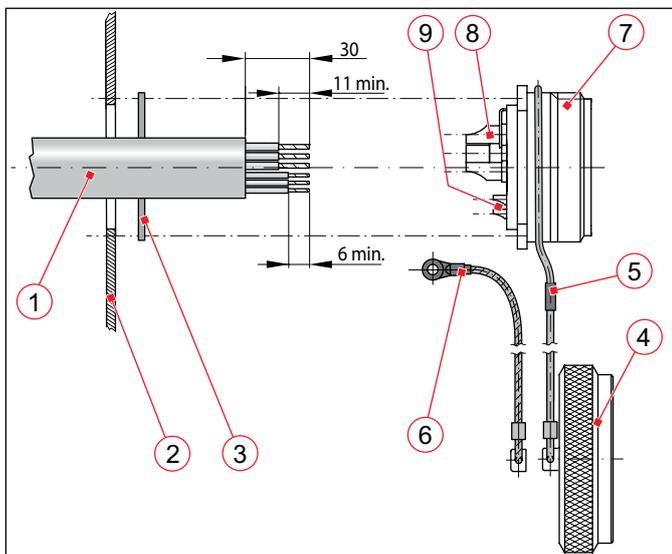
Beispiel für die Montage von Dosen mit Flansch an eine Gehäusewand
